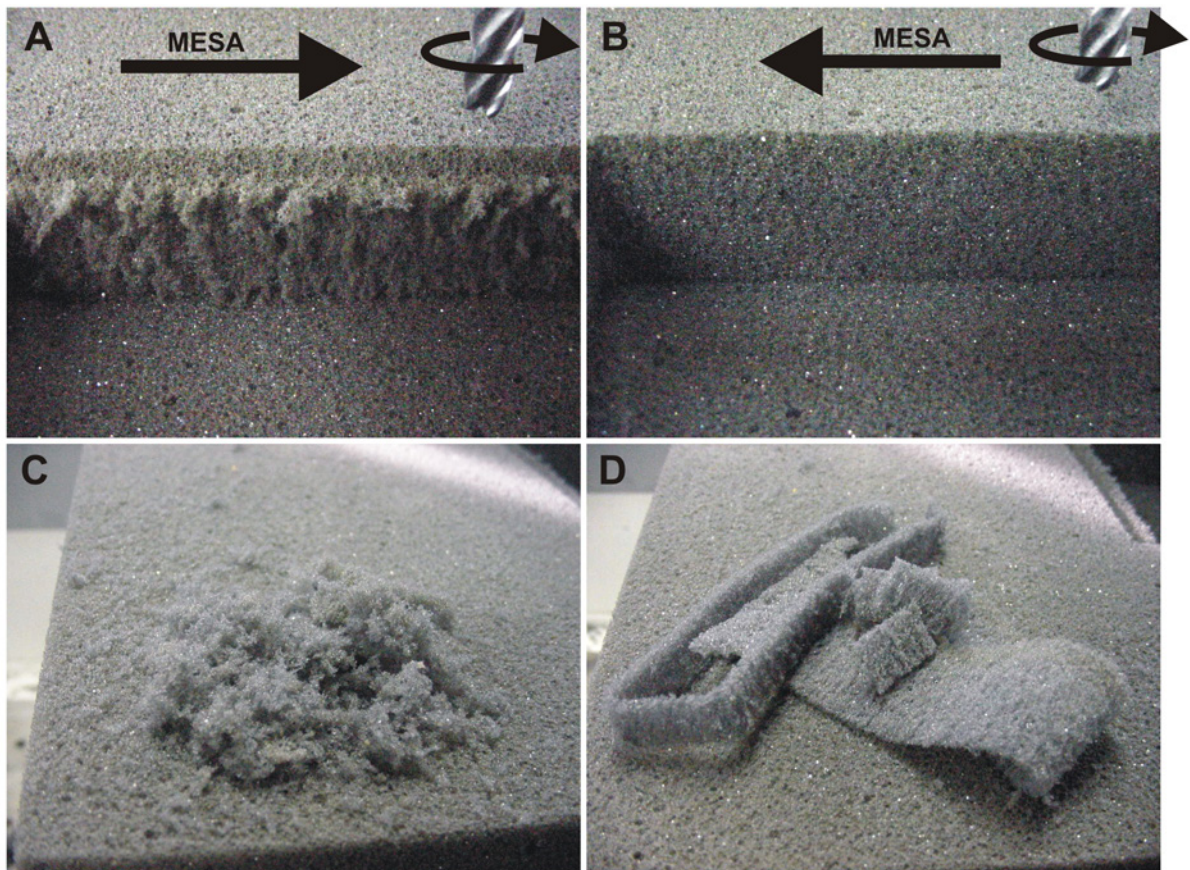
Usinagem concordante (A) e discordante (B) e seus respectivos cavacos (C) e (D).
